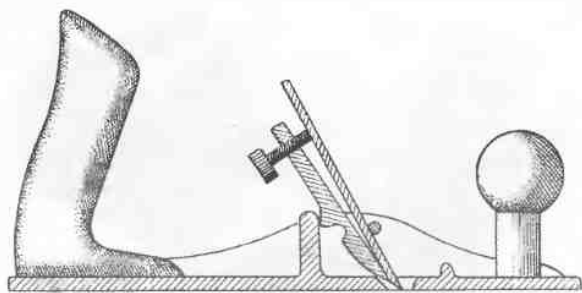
Перестановка крепежного клина рубанка на нижнюю сторону железки для увеличения ее угла наклона (при торцовке и строгании твердой древесины).
